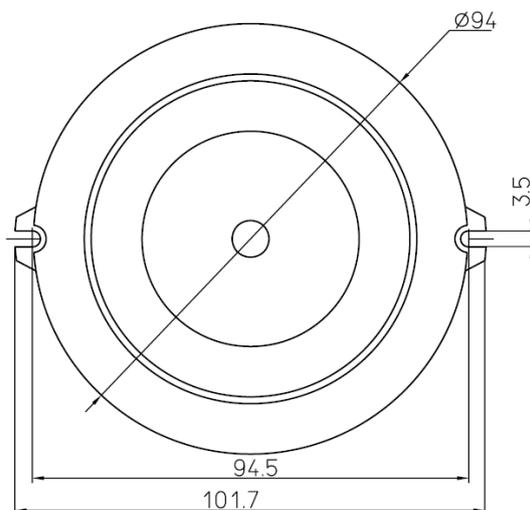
Габаритные и присоединительные размеры корпуса ОСЗ
